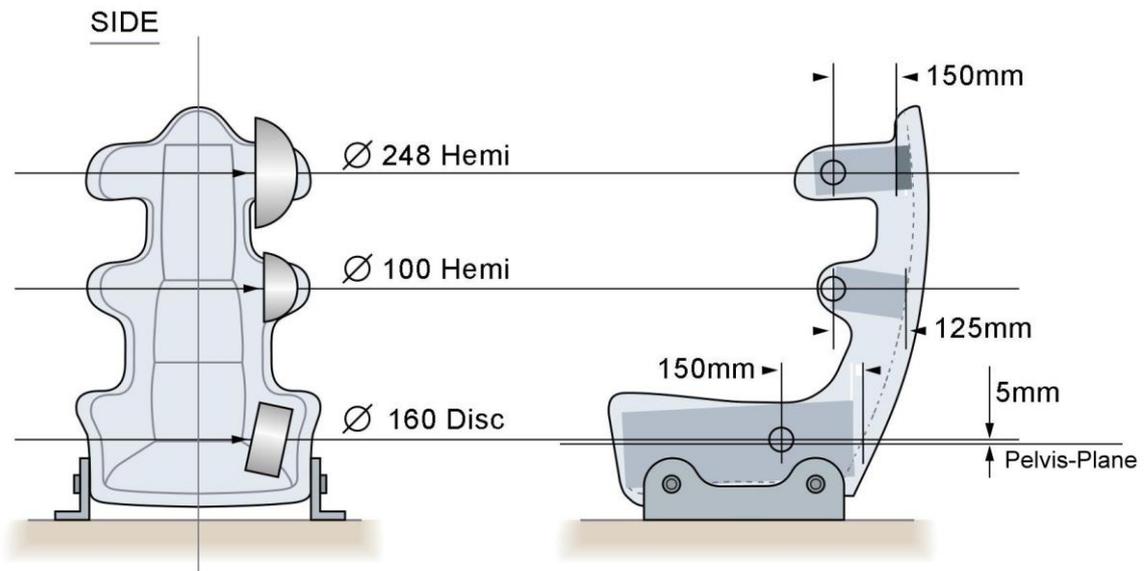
Configuration d'essai pour l'application d'une charge dans la direction latérale
